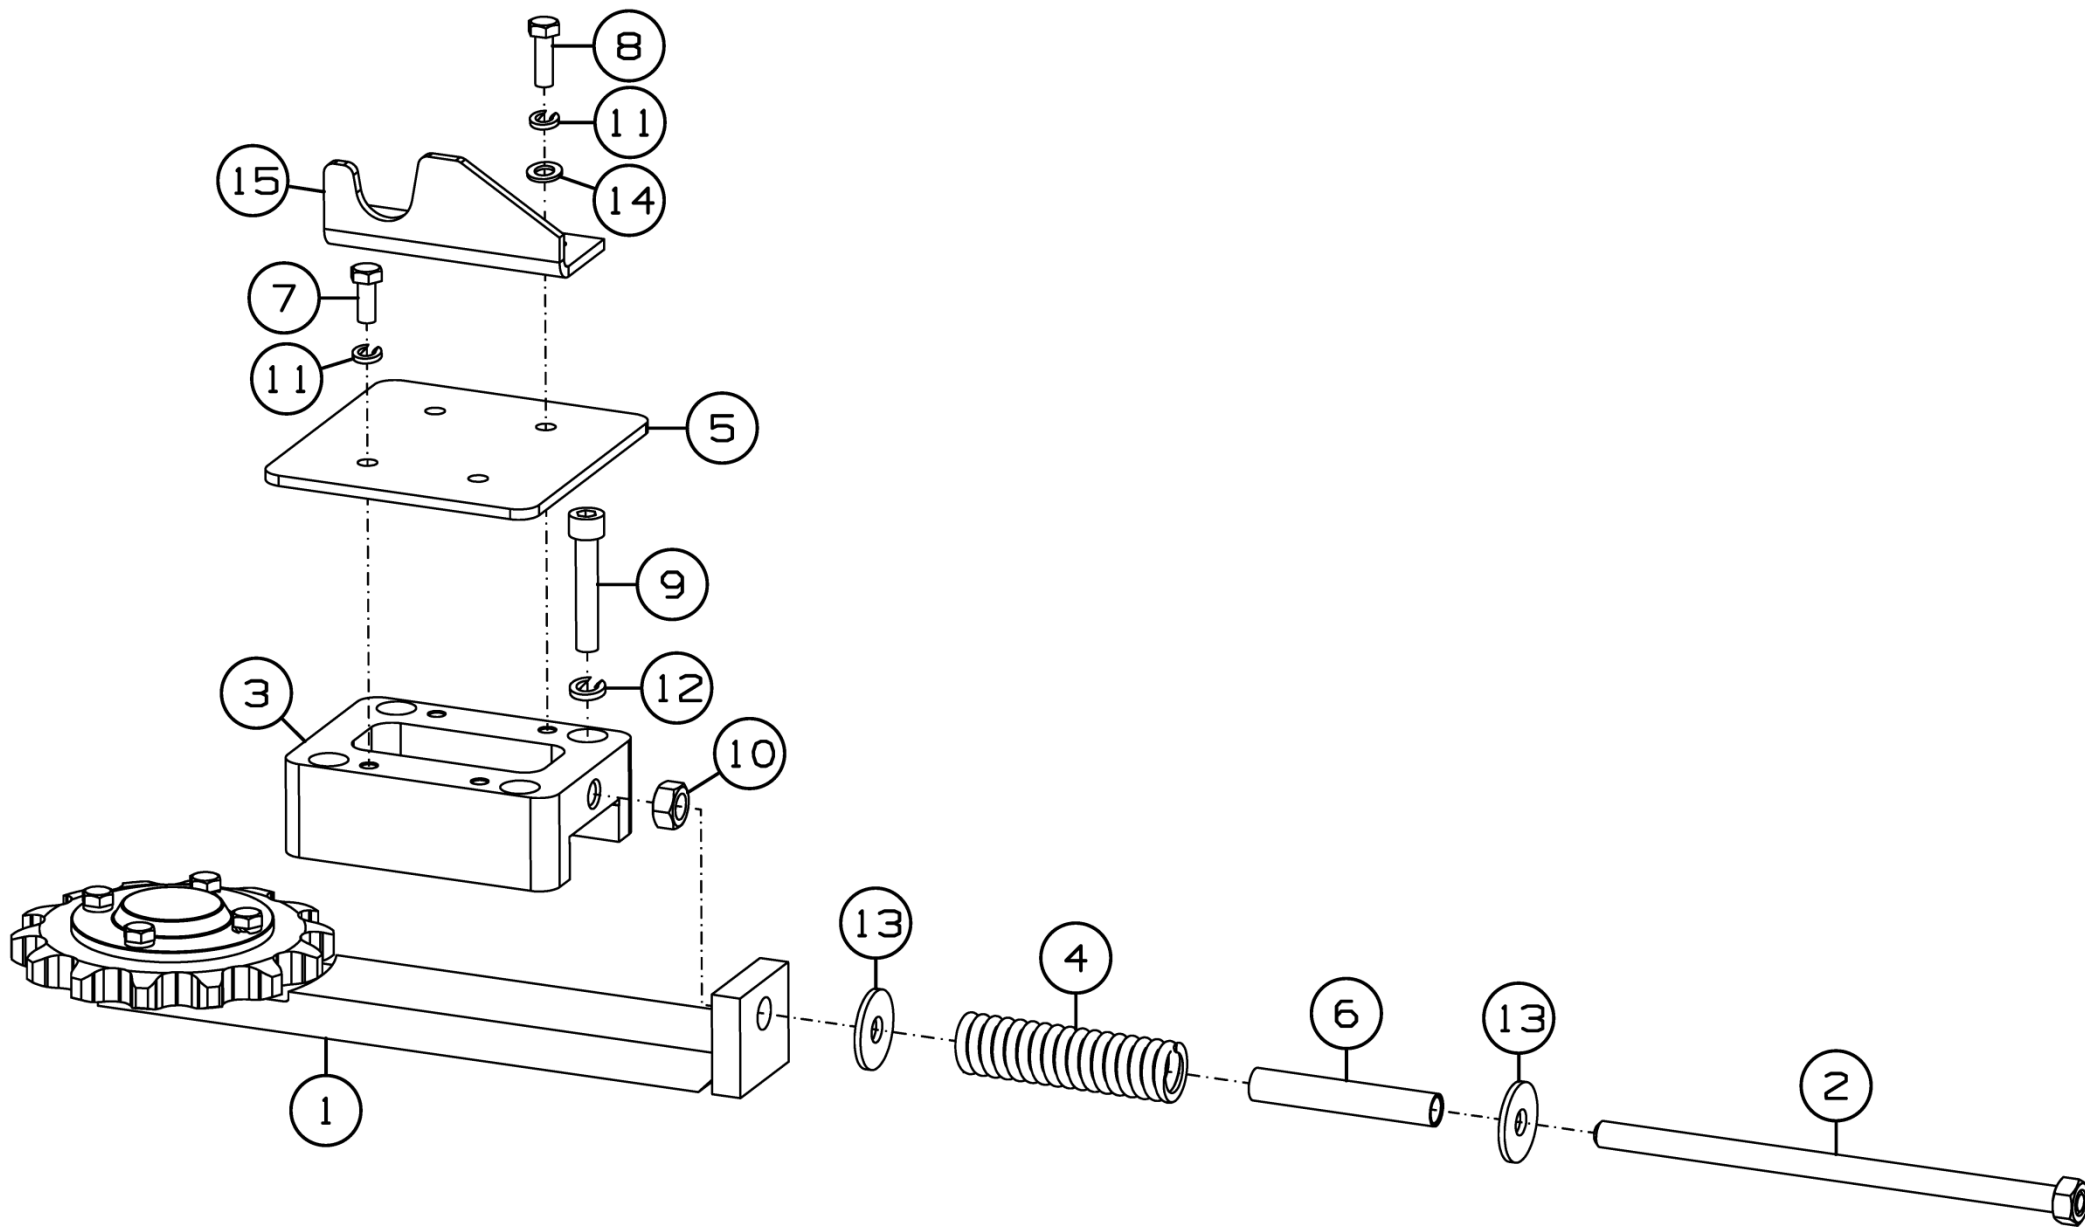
Установка натяжного устройства ППК-870.01.06.110А
